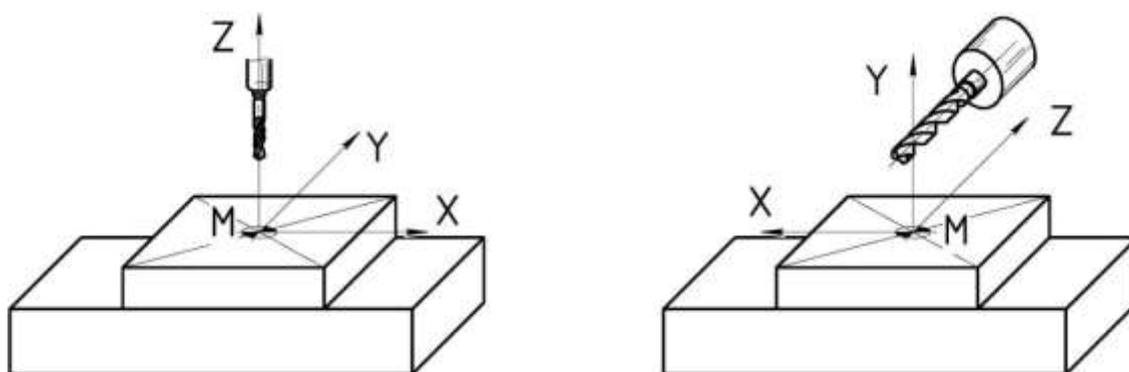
Типовые системы координат фрезерных, сверлильных и расточных станков с ЧПУ
